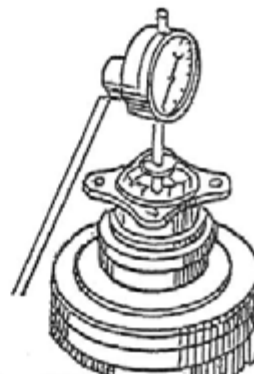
Замер осевого люфта в подшипниках ведущей шестерни
